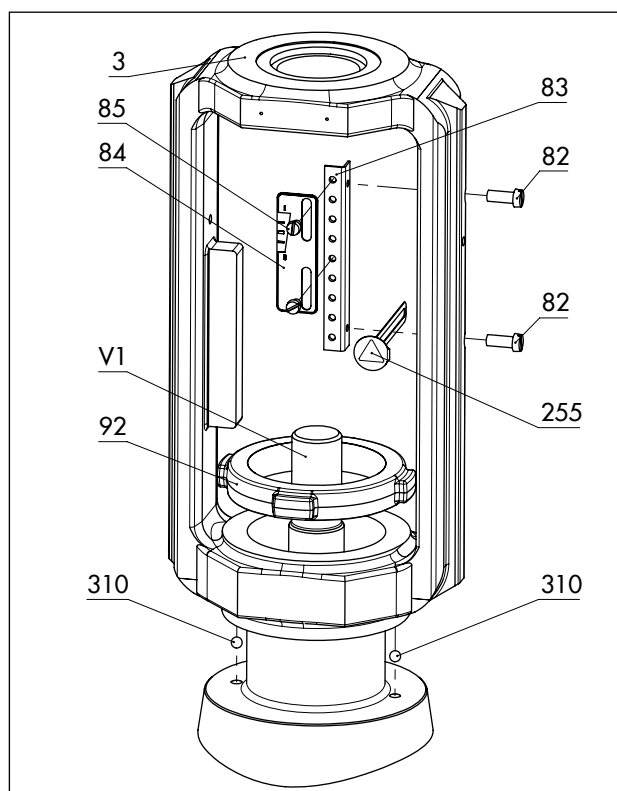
Montaje del puente con placa indicadora de carrera en la ejecución estándar
